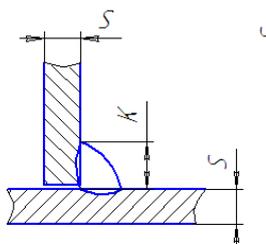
Соединение Т1 -Δ5 по ГОСТ 14771-76, сварной шов №1
